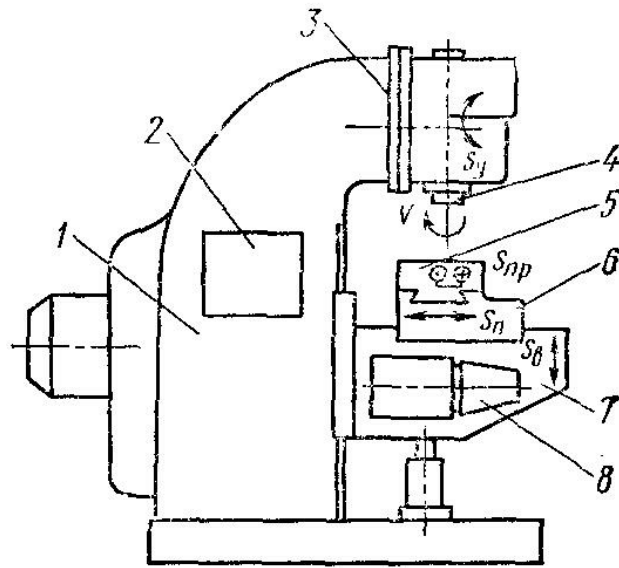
Загальний вигляд вертикально-фрезерного верстата
